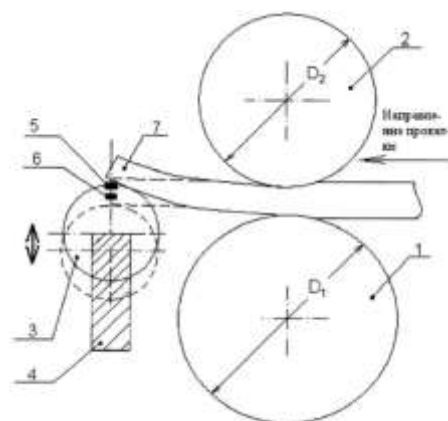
Устройство для асимметричной прокатки: 1 – нижний валок; 2 – верхний валок; 3 – отгибующий ролик; 4 – механизм перемещения; 5 – датчик положения; 6 – индикатор наличия металла; 7 – лист
